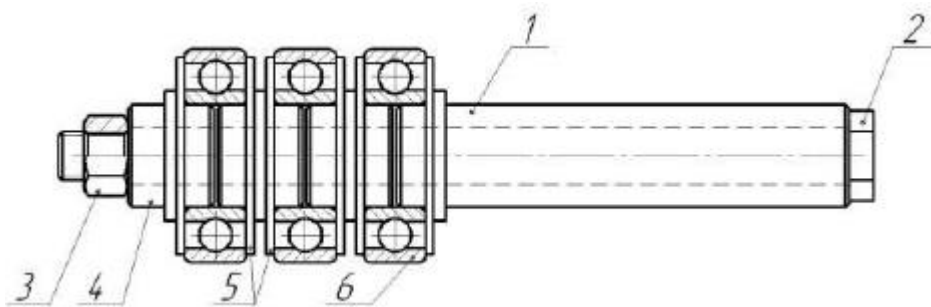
Центруюча монтажна оправка: 1 - вал; 2 - затискний гвинт; 3 - натискна гайка; 4 - centruючий ролик; 5 - шайба; 6 - підшипник.
